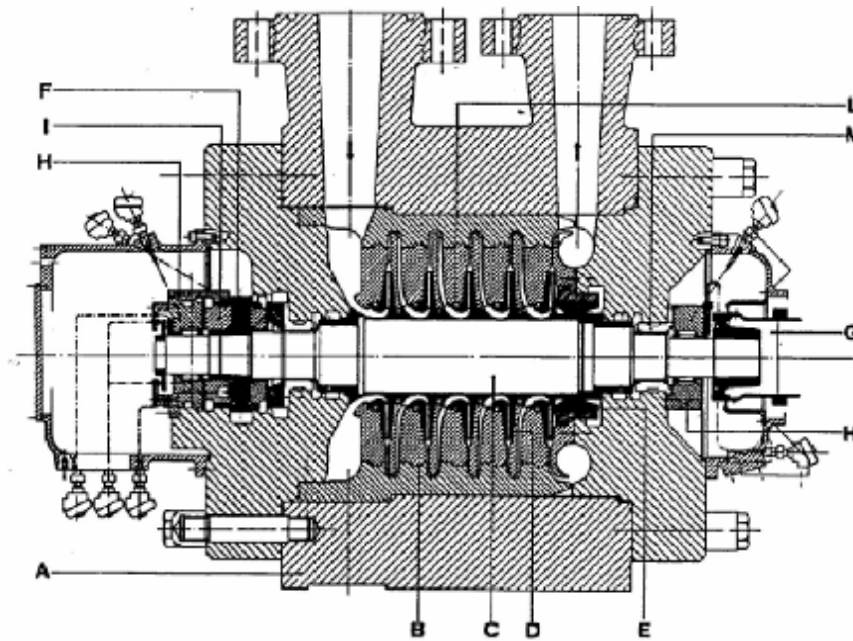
Coupe longitudinale d'un compresseur centrifuge
